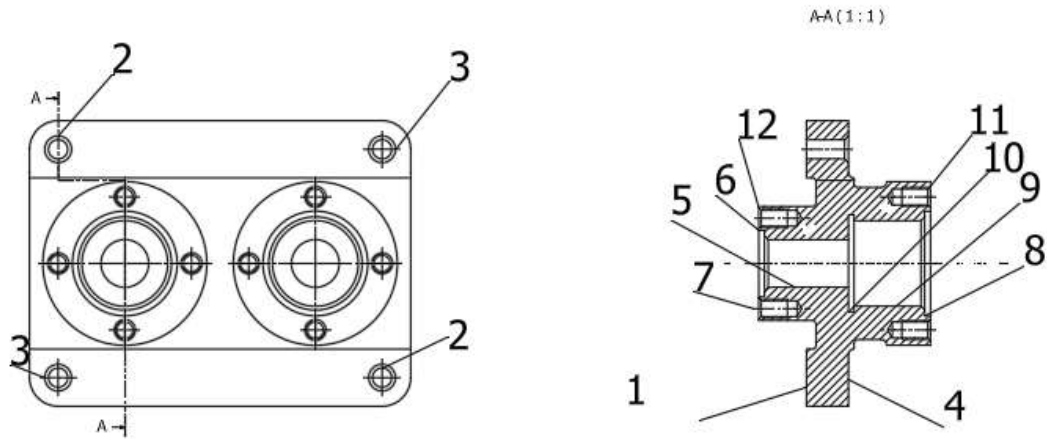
Ескіз деталі із зазначеними під обробку поверхнями
